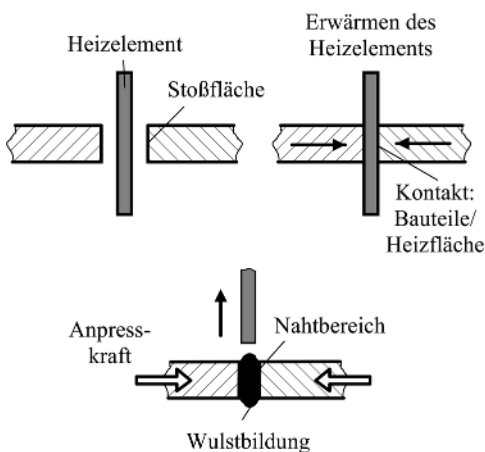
Prinzip des Heizelementschweißens bei Kunststoffen.
